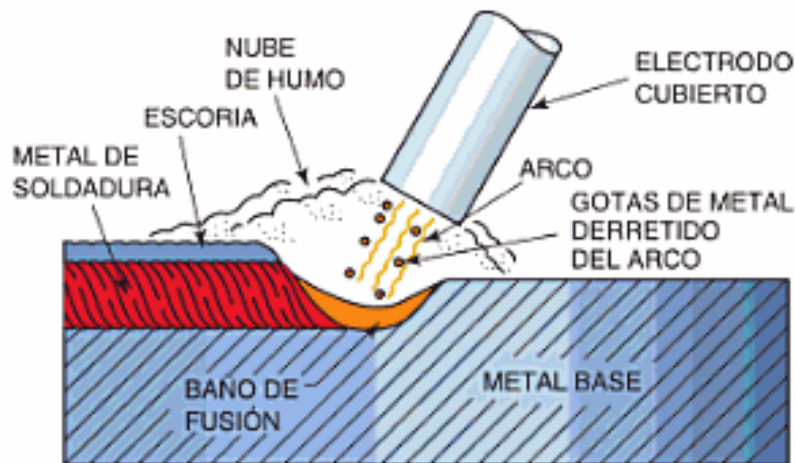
Soldadura SMAW. (Jeffus, 2009)
